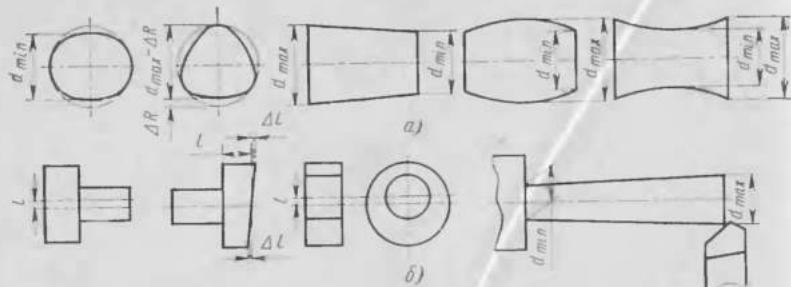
Схемы основных погрешностей обрабатываемых деталей
